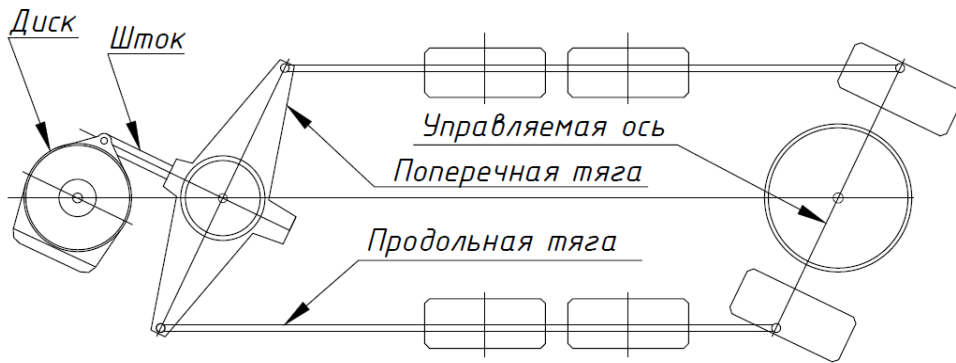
Схема поворотного устройства полуприцепа Welgro
